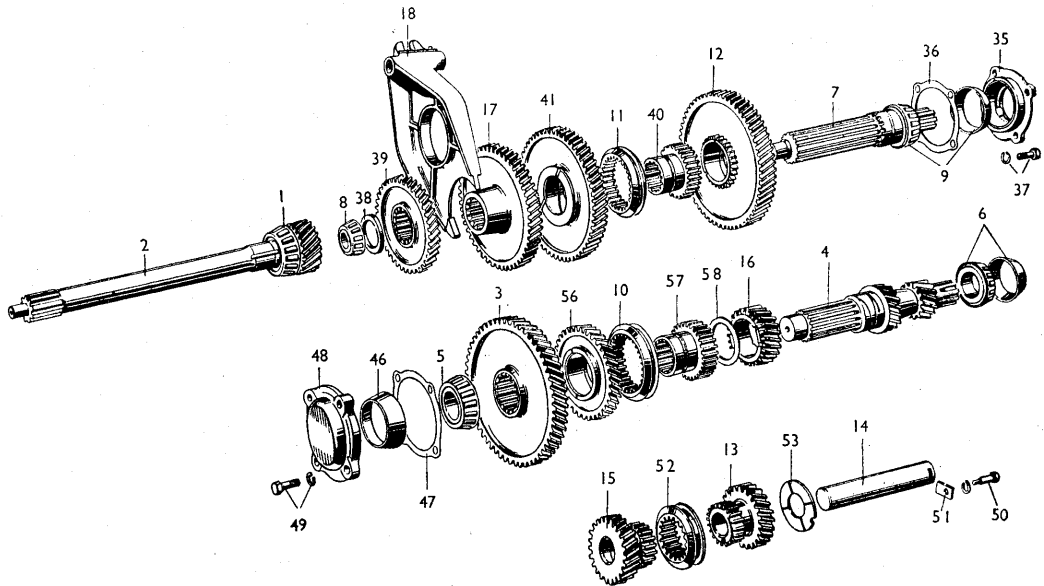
Exploded-view af gearkassens aksler og hjul.
